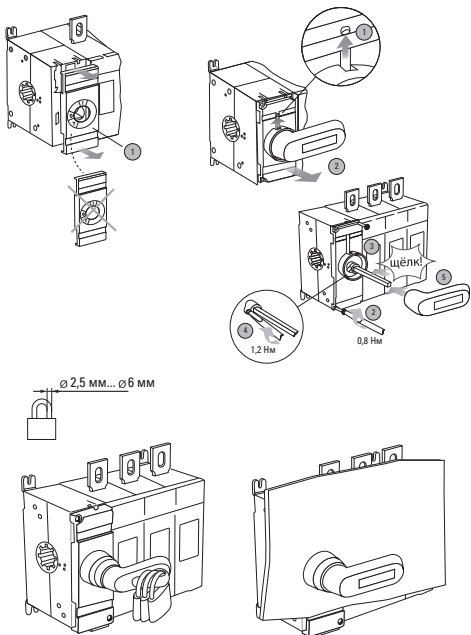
Установка рукоятки управления прямой установки 315-2500А
